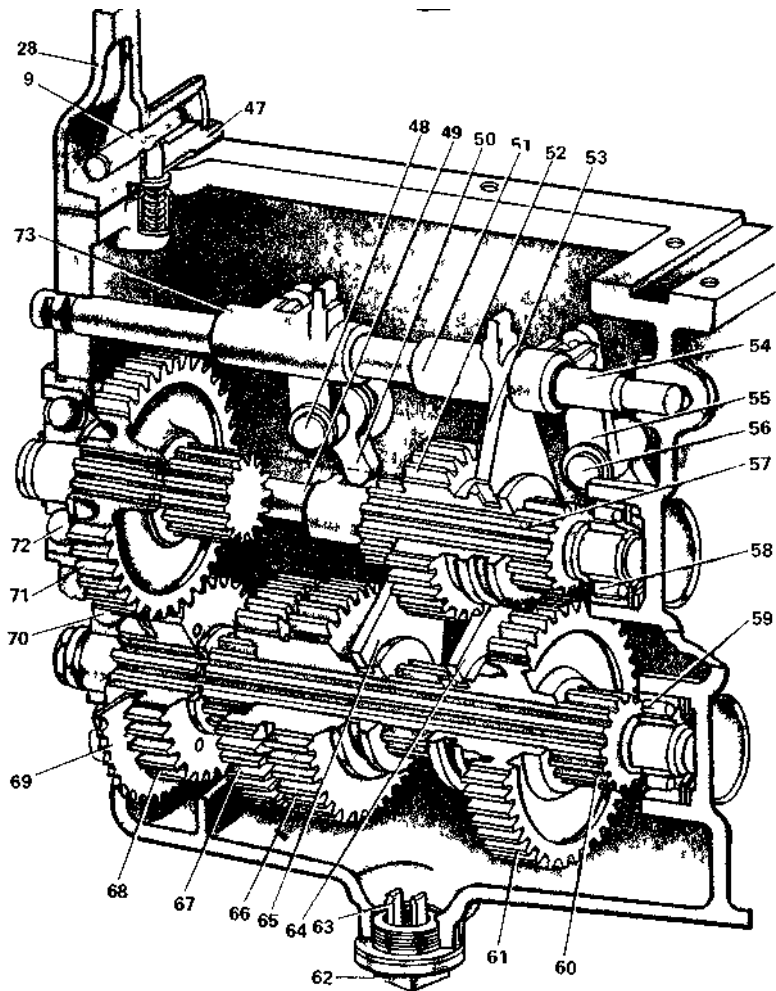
б- Коробка передач трактора ДТ-75МВ:
